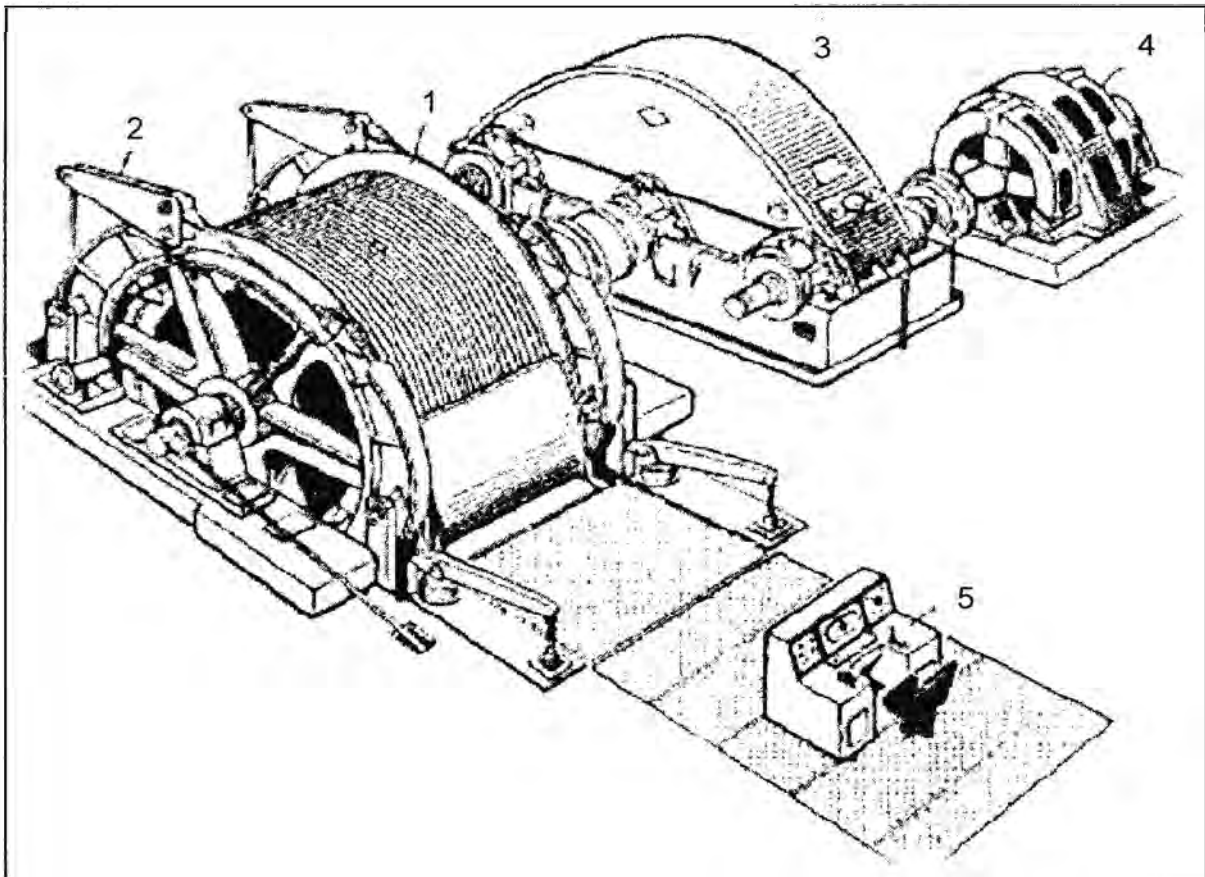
Máquina de elevación con un tambor cilíndrico
